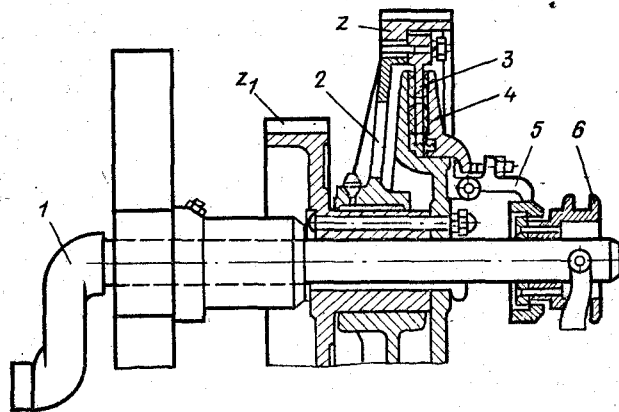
Схема передачи движения к главному валу станка АТ-100-5
